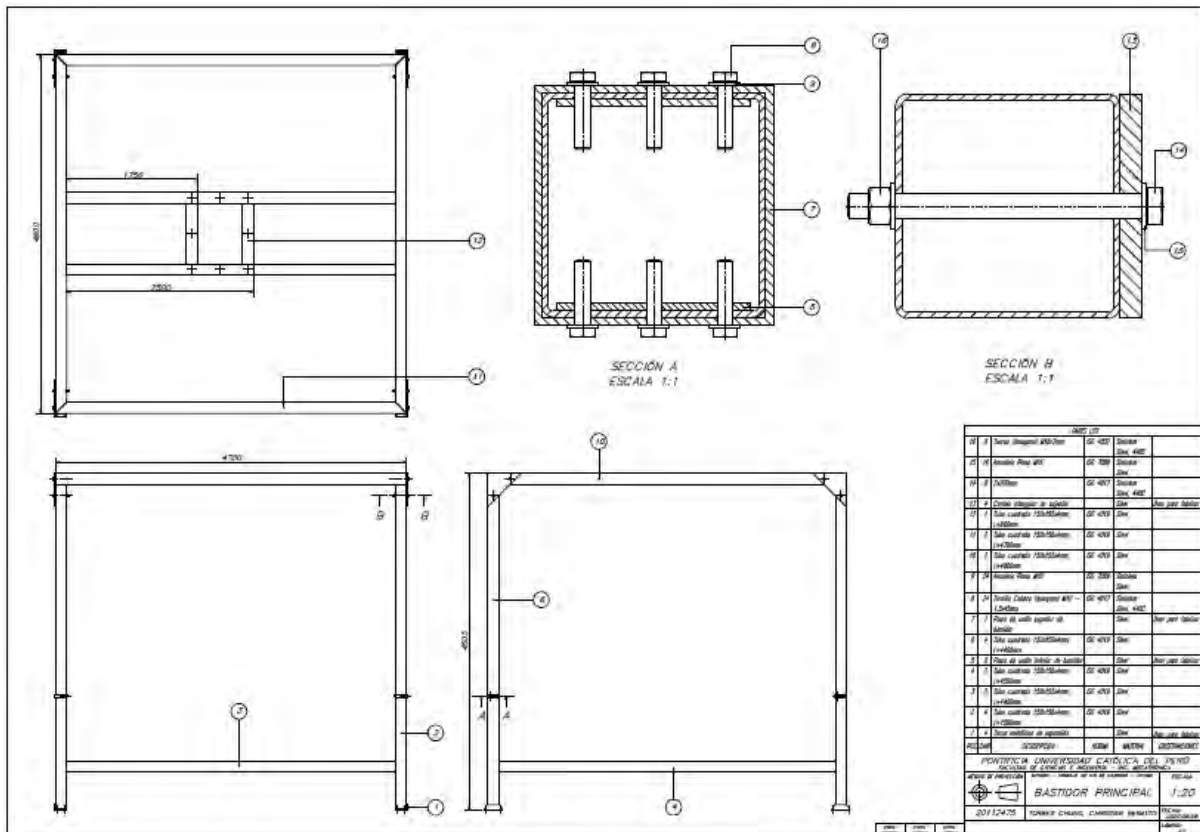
Estructura del Sistema. Plano. Fuente: Propia.
